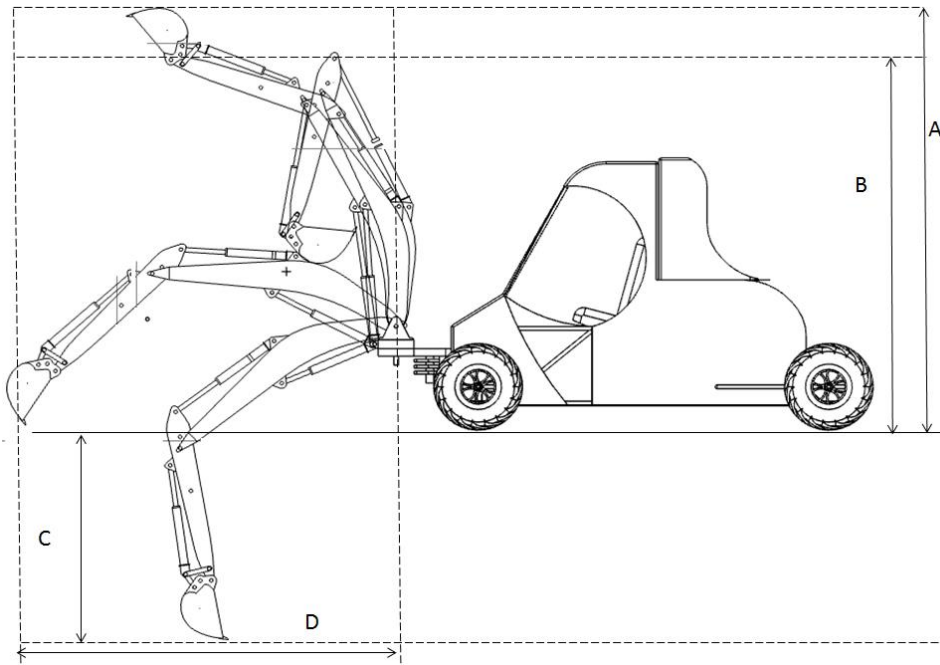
Rango de trabajo vertical del brazo excavador.
